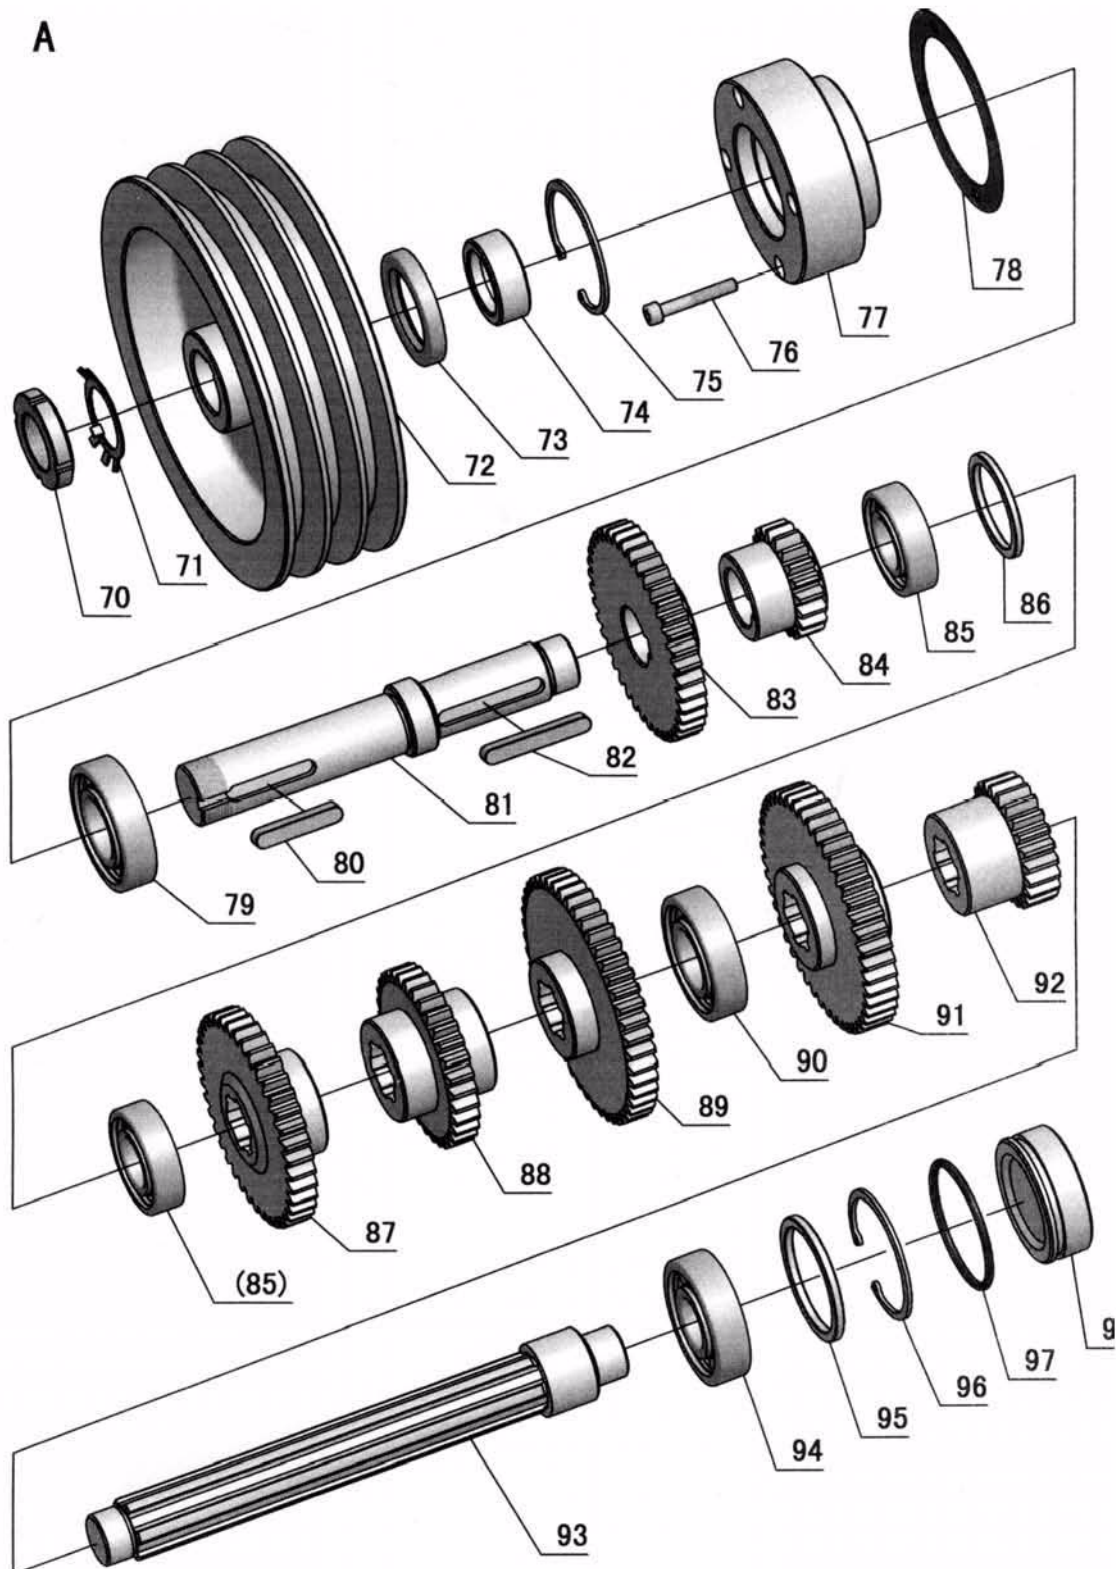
Spindelstock 3 von 8 - Headstock 3 of 8
